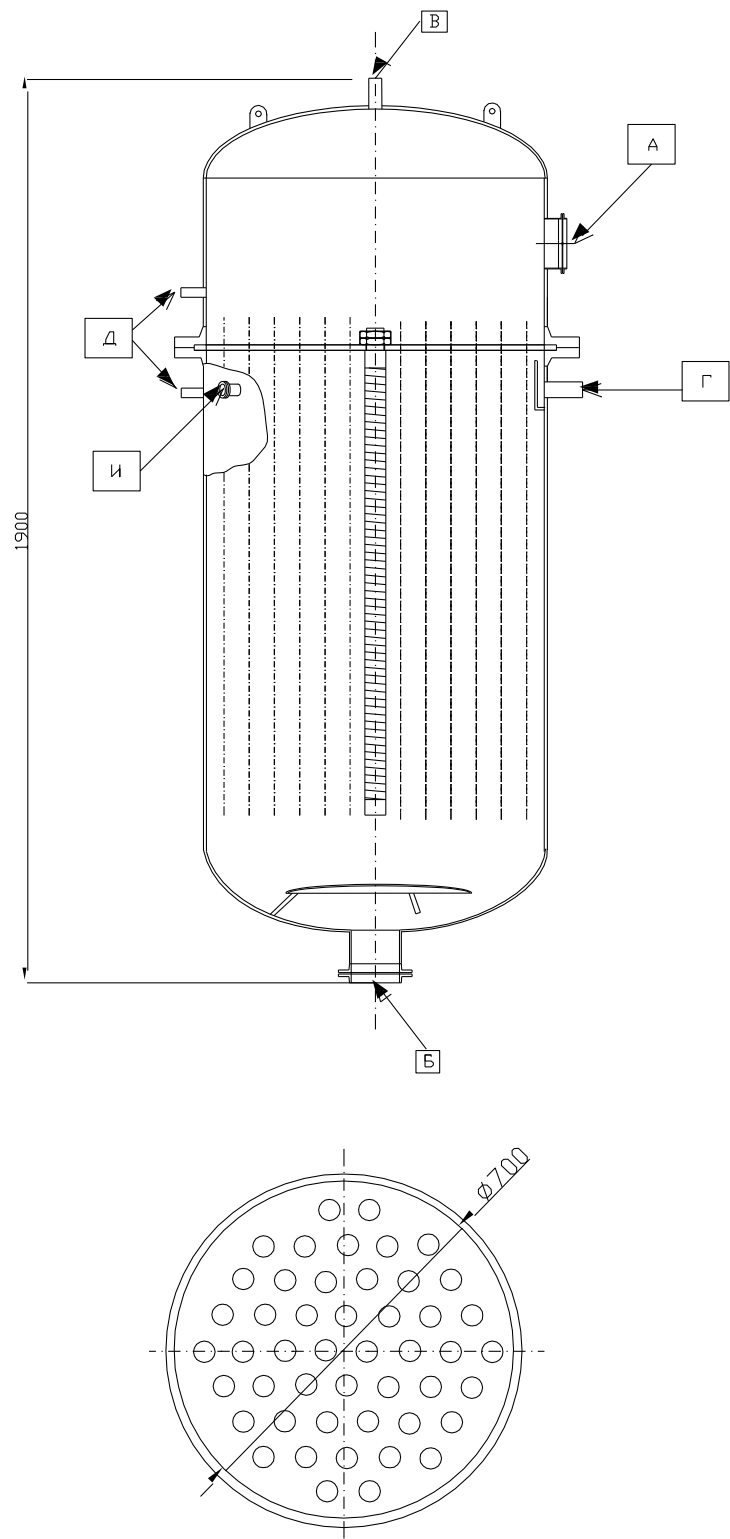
Габаритный чертеж фильтра ионитного намывного FAL30AT001,
